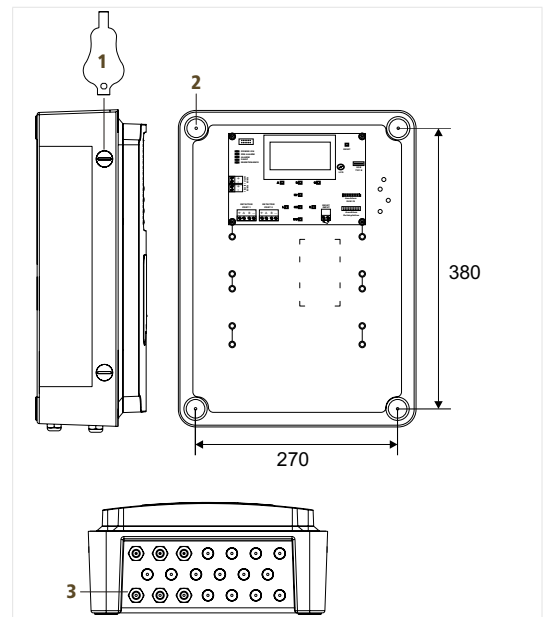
Abmessungen für Montagelöcher (Angaben in mm)
